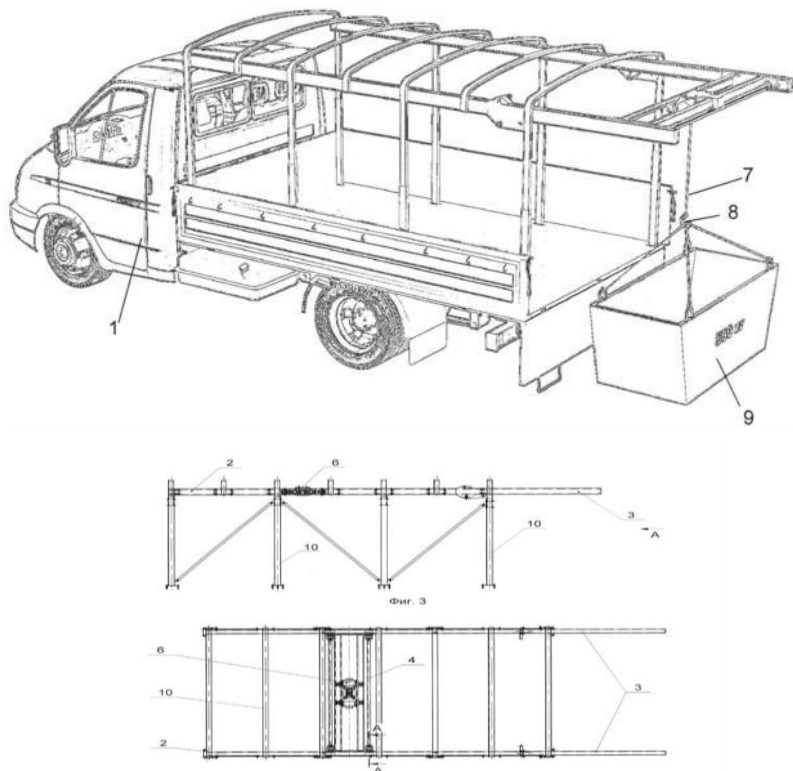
Конструкция контейнерного подъемного крана: 1 – грузовой автомобиль; 2,3 – направляющие(поворотные) рельсы; 4 – двухопорная балка; 5 – опорные ролики; 6 – грузоподъемное приспособление; 7 – канат; 8 – крюк; 9 – груз; 10 – стойки
